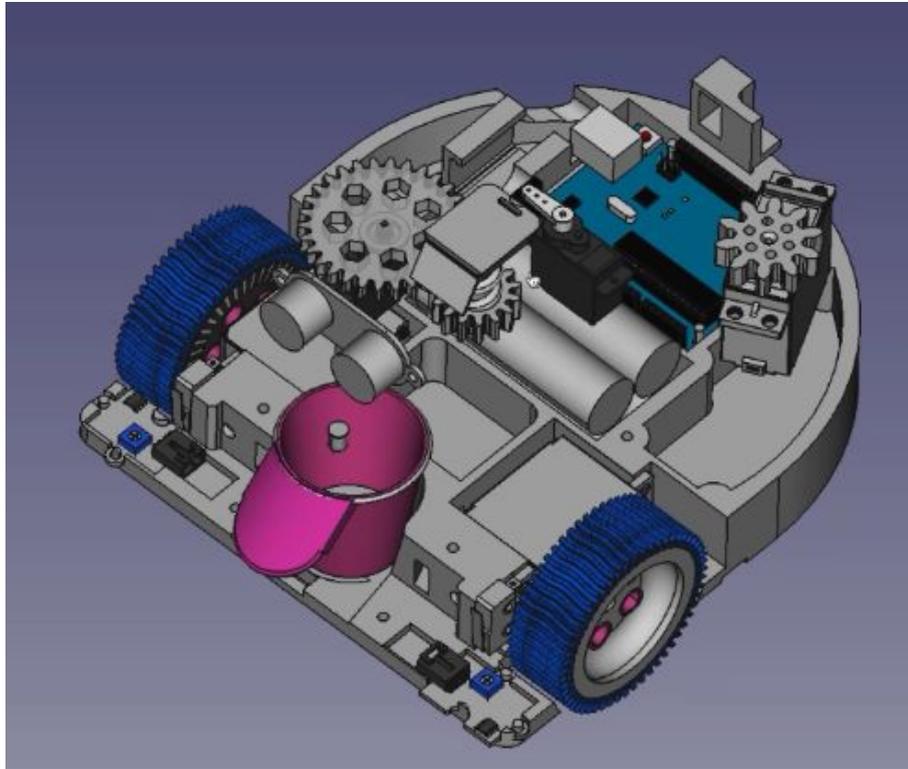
Diseño en Freecad montaje. E. Dorado
